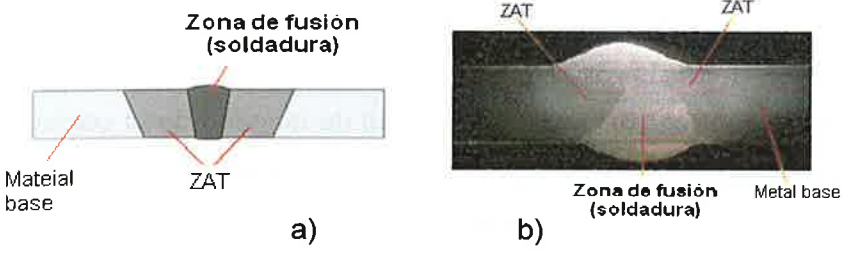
(a) Representación esquemática de la sección transversal de una unión soldada por TIG, y (b) zonas identificadas en una unión soldada de un acero al carbono.
